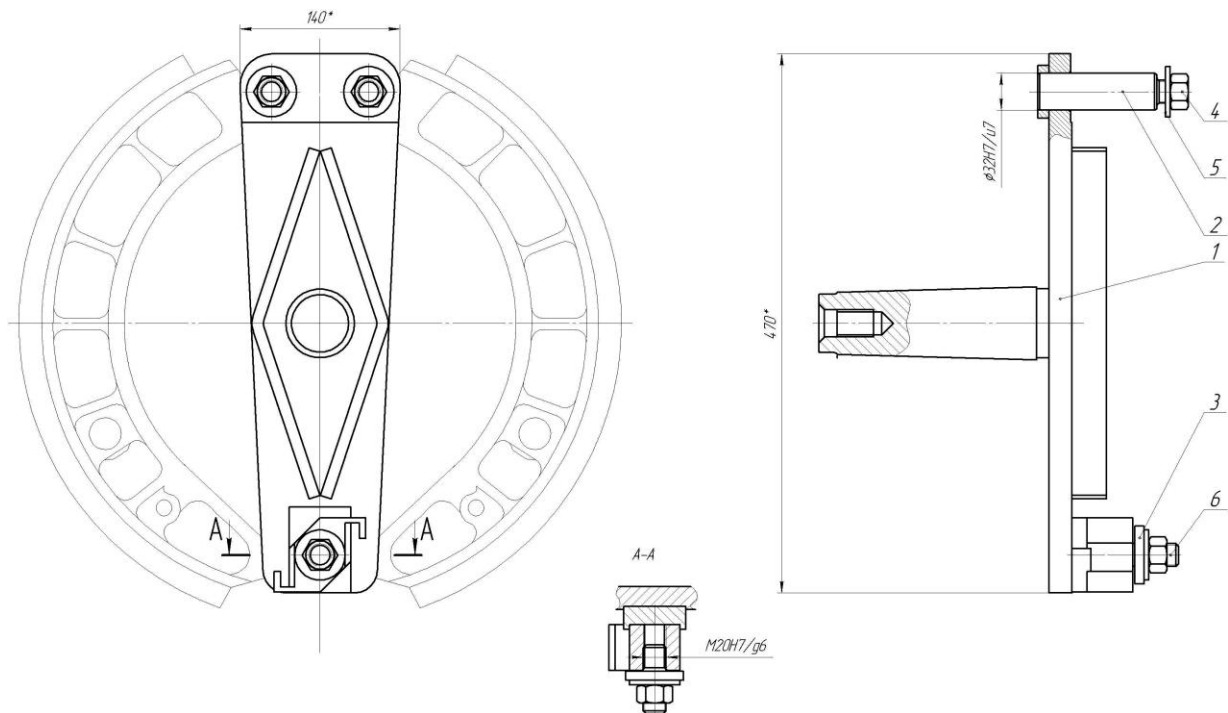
Приспособление ПТ-1880 ГОСНИТИ
